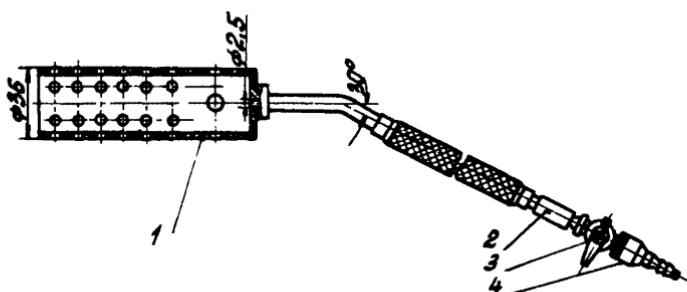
Горелка ИЗ55.05.03 конструкции СКБ Газстроймаша:
